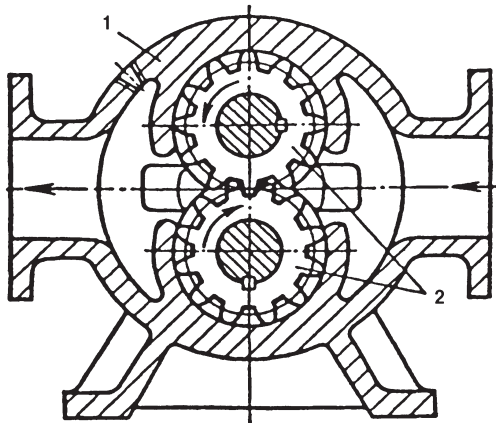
Схема шестеренного насоса: 1 – корпус; 2 – зубчатое колесо
